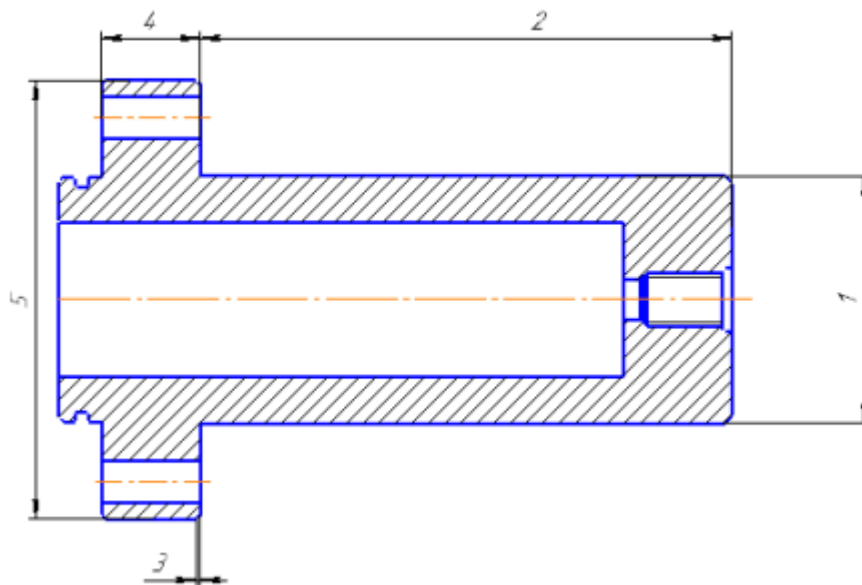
Креслення оброблюваної деталі з необхідними розмірами
